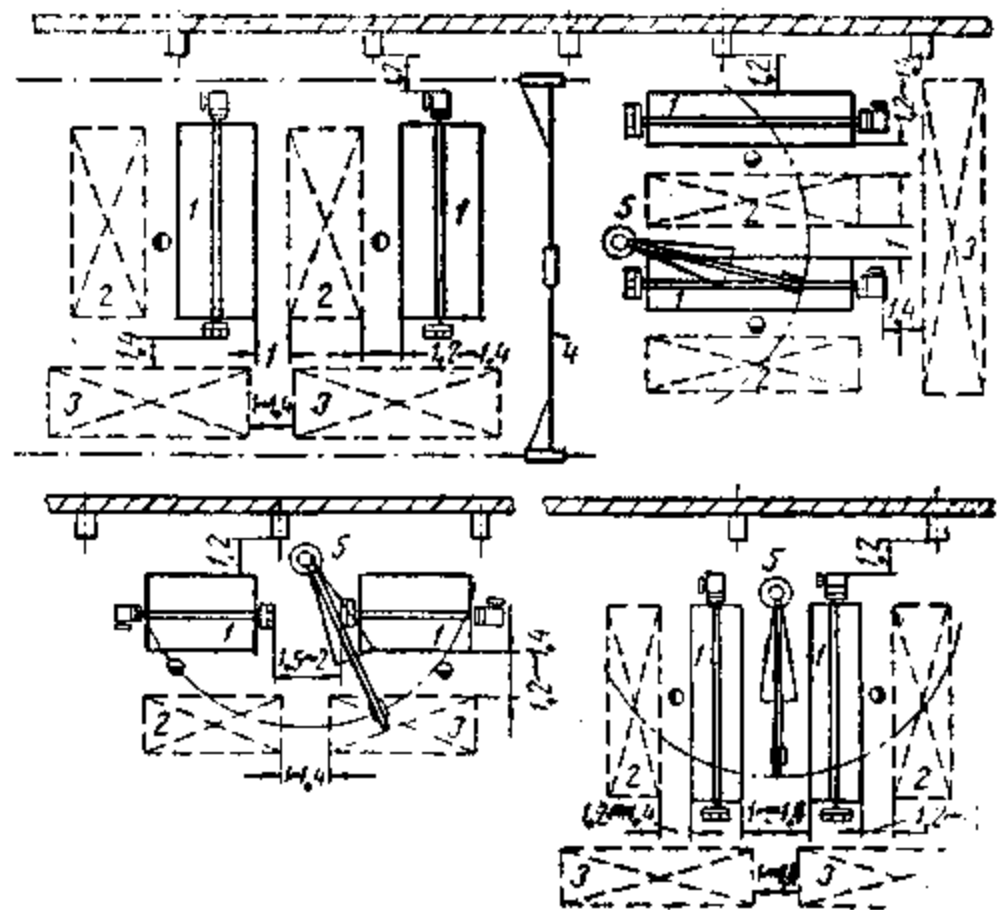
可移动的双柱式焊接翻转机平面布置图
